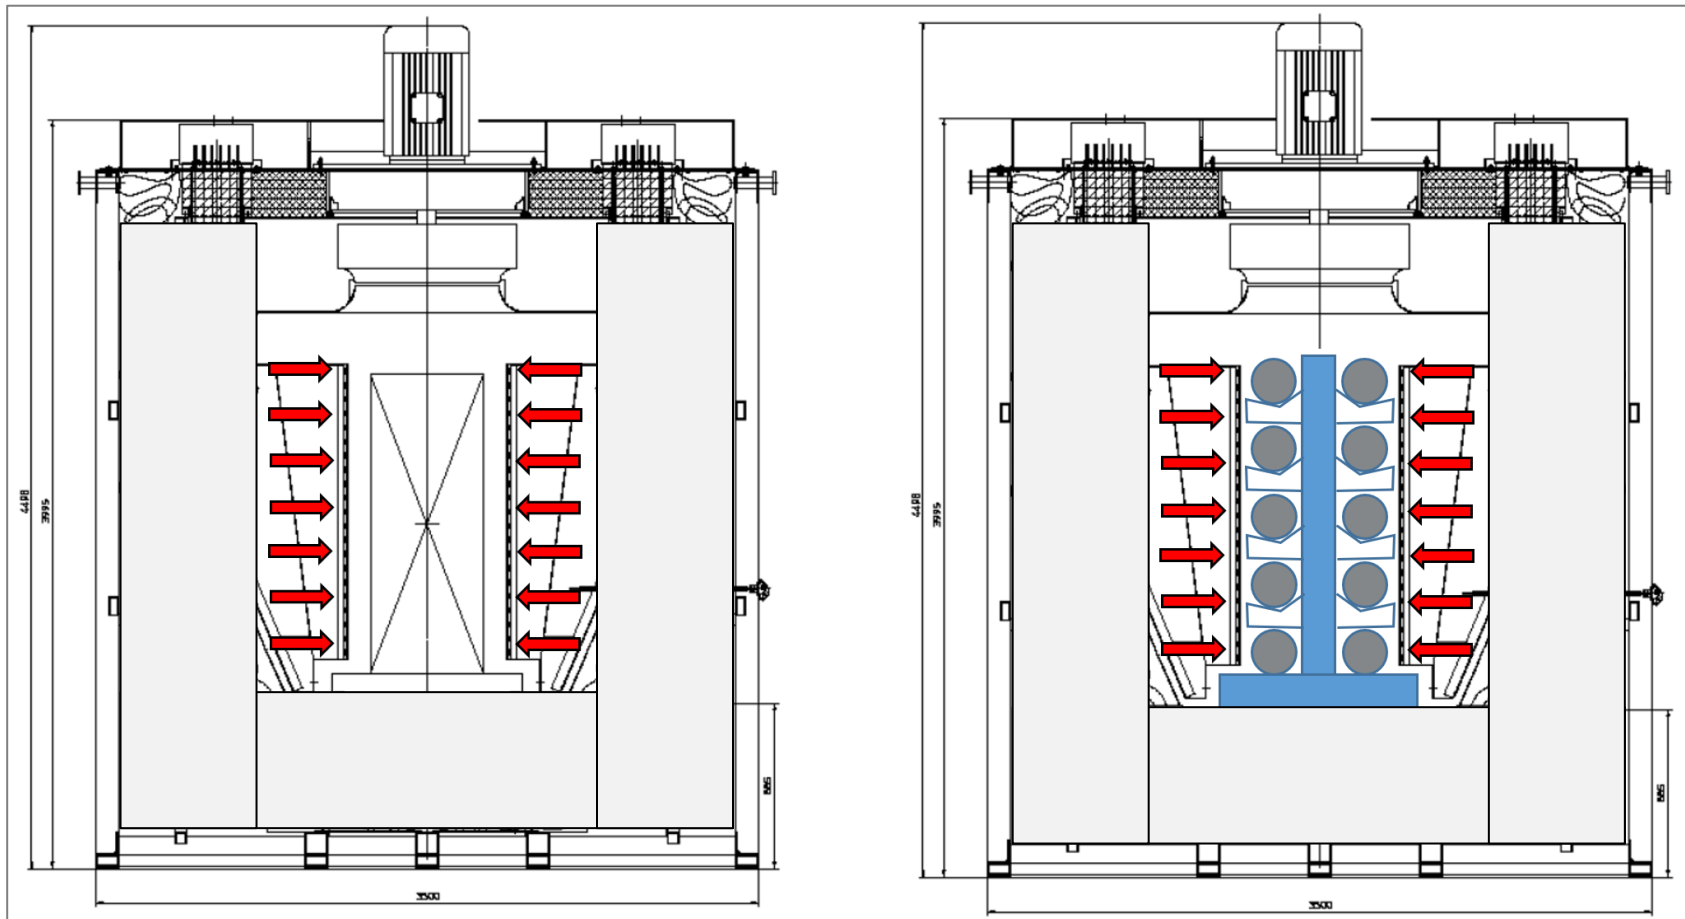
Kammerofen mit Jet-Heating zum Erwärmen von Aluminiumbolzen und -barren
